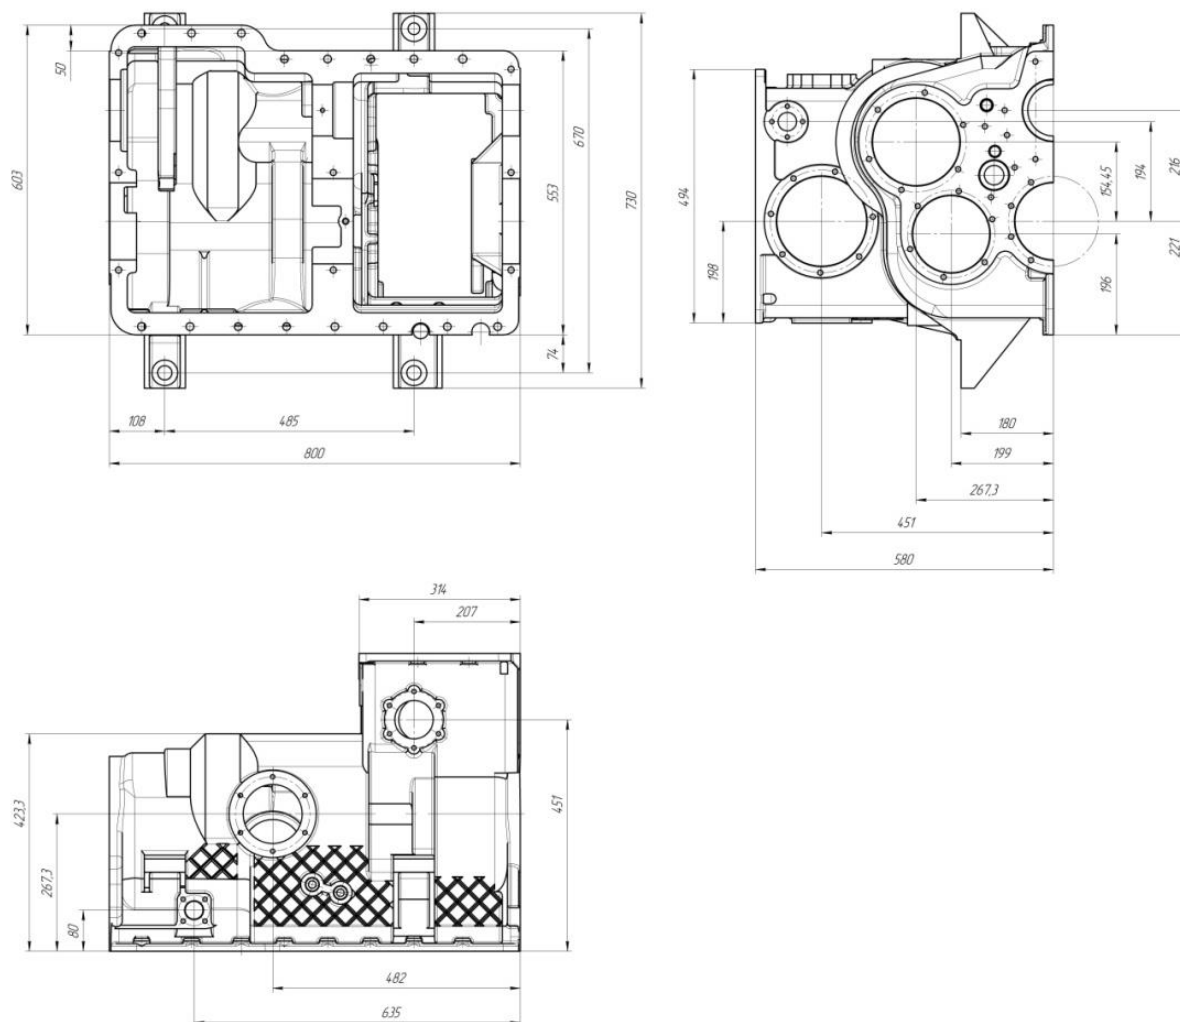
Присоединительные размеры картера КПП нижней
